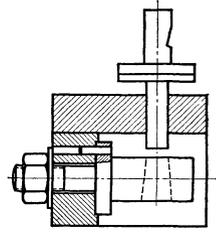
Befestigung einer hornförmigen Schnittplatte.
